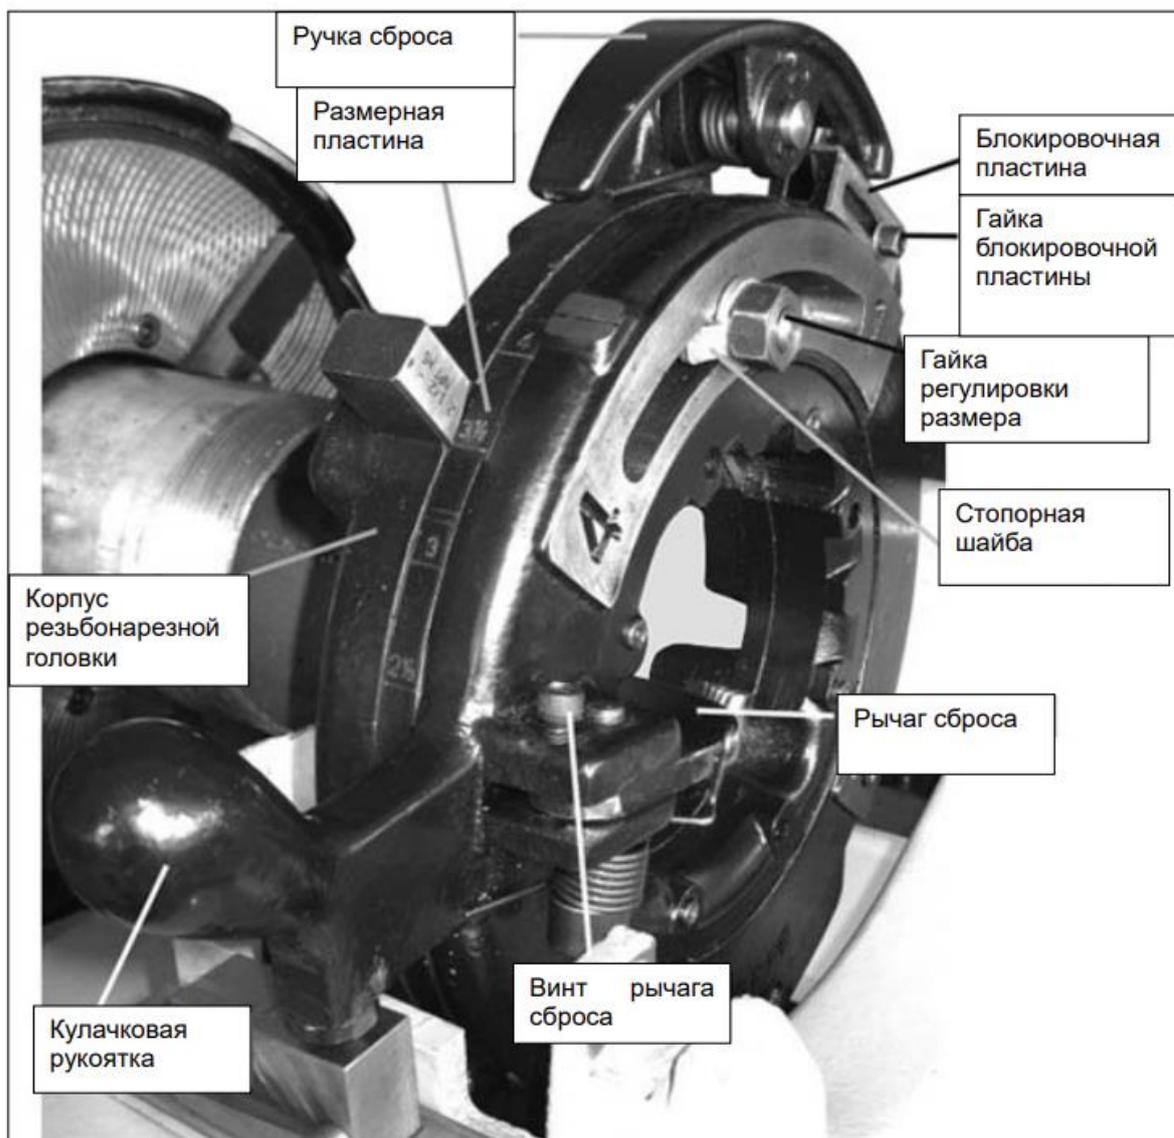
Установка резьбонарезных ножей 2 1/2"-4"
